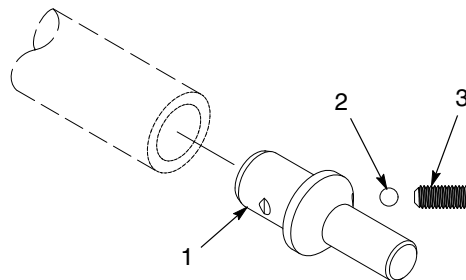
Kit adaptateur pour pistolets Versa-Spray
